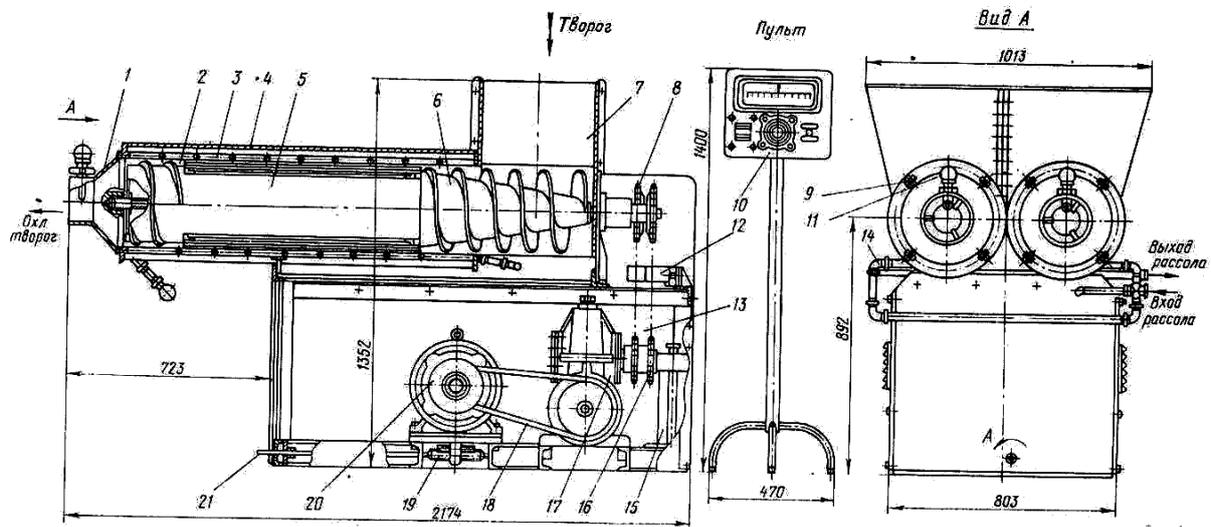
Общий вид охладителя творога двухцилиндрового марки ОТД: 1 – крышка; 2 – цилиндр; 3 – рубашка; 4 – кожух; 5 – барабан вытеснительный; 6 – коническая часть корпуса барабана; 7 – бункер; 8 – ведомые звездочки; 9 – зажим; 10 – пульт; 11 – термометр сопротивления; 12 – натяжное устройство для цепей; 13 – цепные передачи; 14 – трубчатый коллектор; 15 – выносная опора; 16 – ведущая звездочка; 17 – червячный редуктор; 18 – клиноременная передача; 19 – механизм для натяжения ремней; 20 – двигатель; 21 – винт
